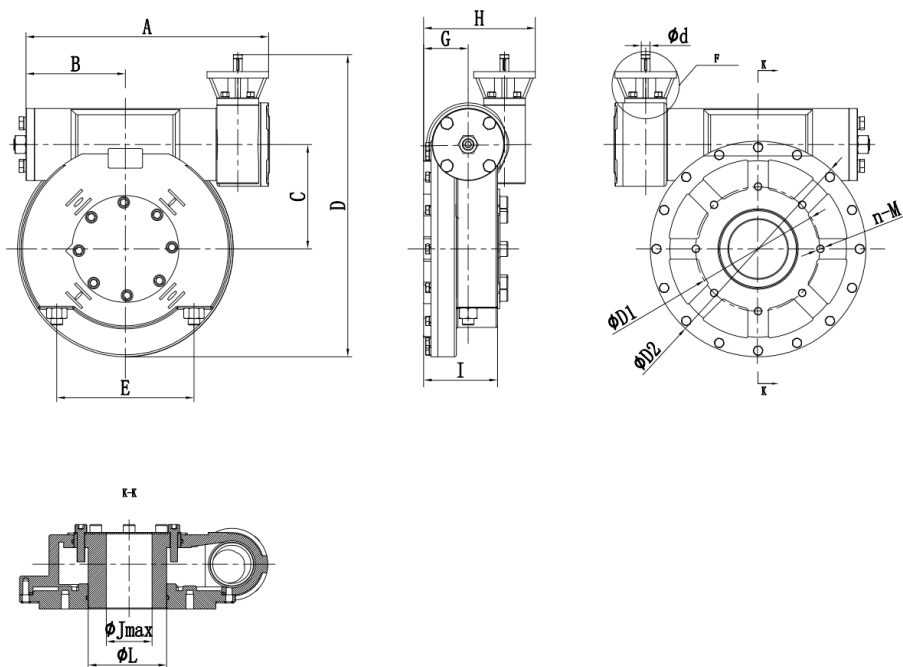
Габаритные размеры редукторов типоразмеров В-IX – В-XI DN700-DN1200.
